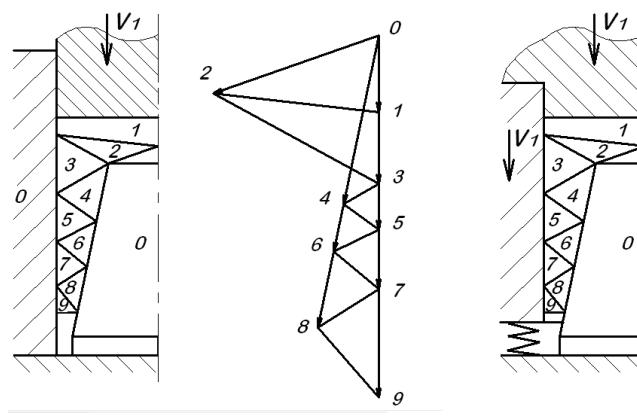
Поля линий скольжения: а) для процесса выдавливания металла в жесткой матрице; в) для процесса выдавливания металла в подвижной матрице; б) обобщенный годограф скоростей
